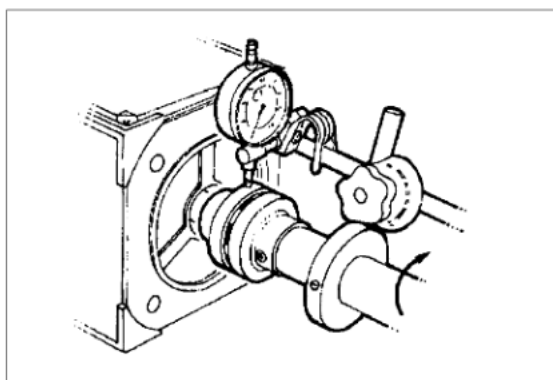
Precisión del acoplamiento directo del eje motor - eje máquina
